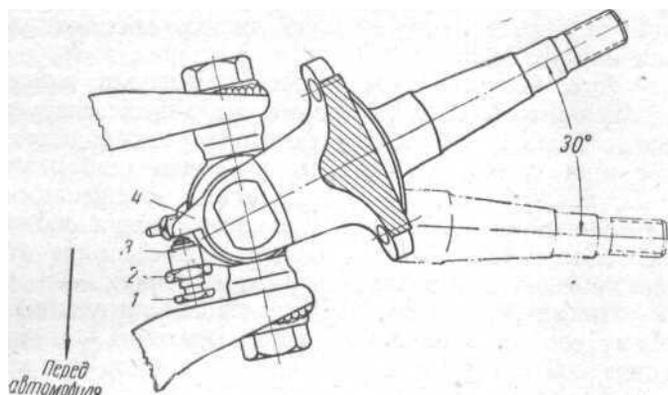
Регулировка угла наибольшего поворота стойки подвески автомобиля модели 403:
